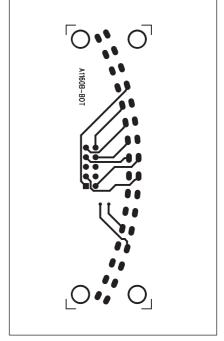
Obrazec desky spojů řídicí jednotky (strana BOTTOM)
